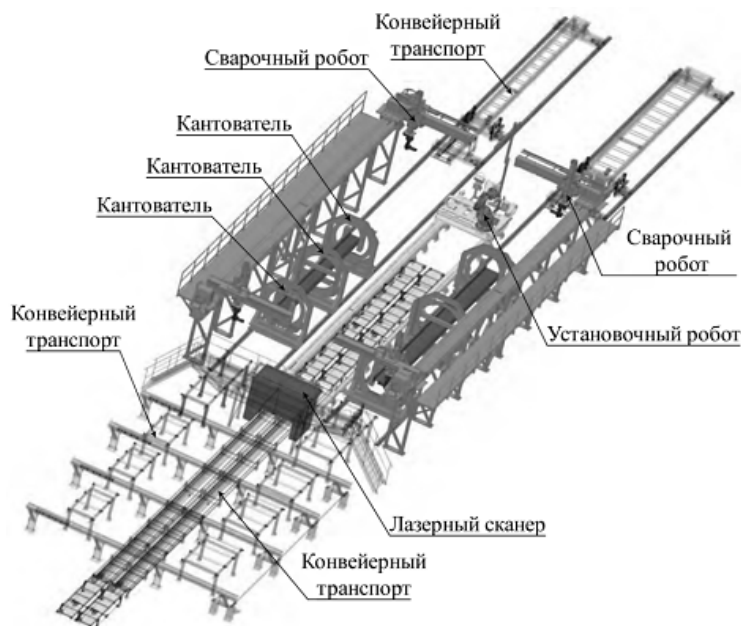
Схема автоматизированной линии сборки и сварки металлоконструкций компании *ZEMAN
